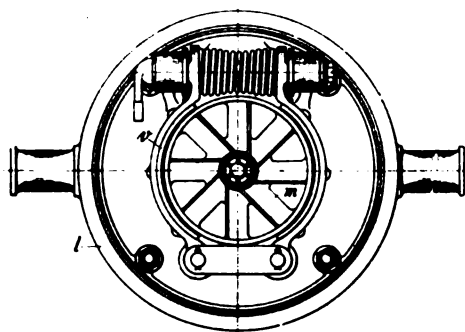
Automobile elettrica. - Tamburo di frenatura.
